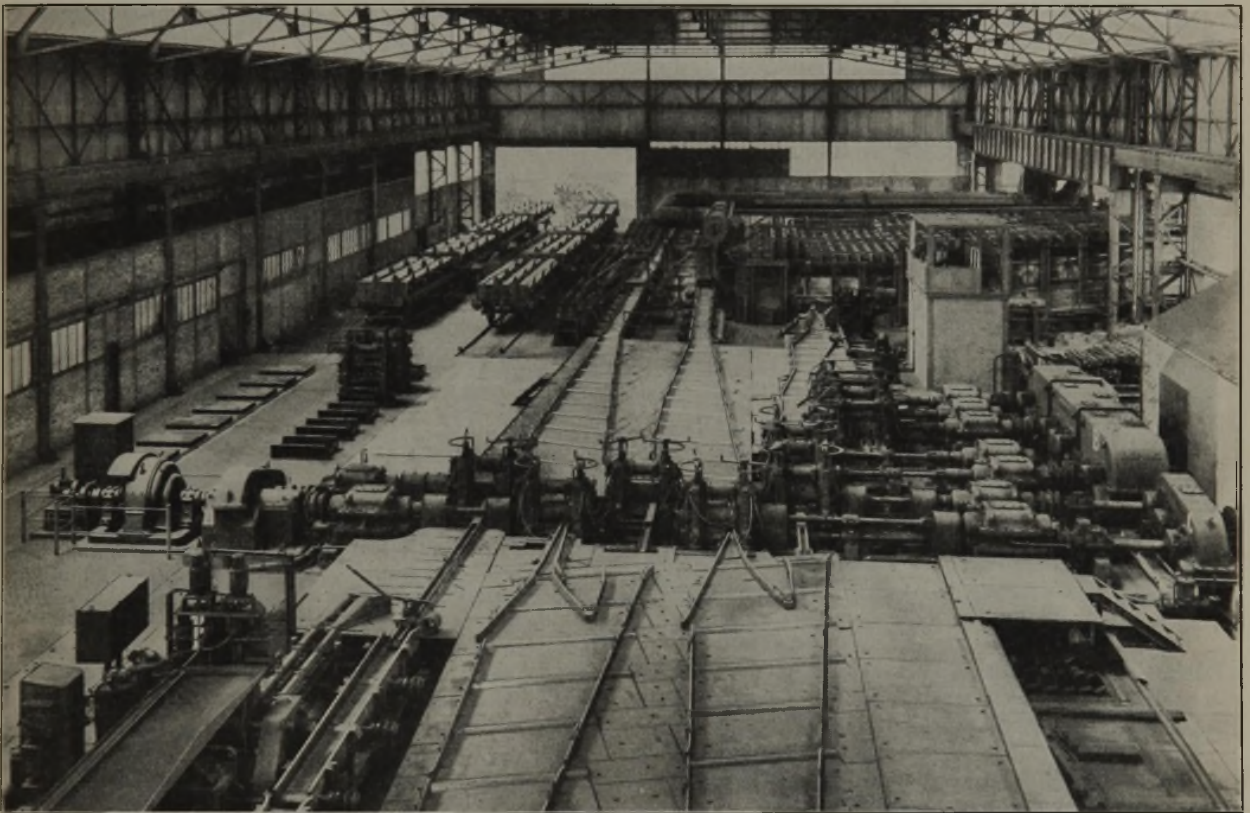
Feinstahl- und Drahtwalzwerk eingerichtet zum Walzen von Profilstahl.
